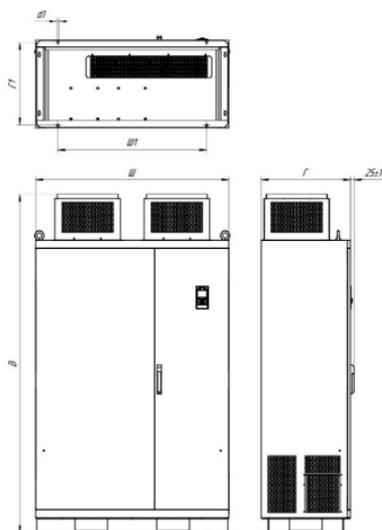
Габаритные и установочные размеры устройств серии INPRIME MX в металлическом корпусе (напольное исполнение), типоразмеры 14-16
